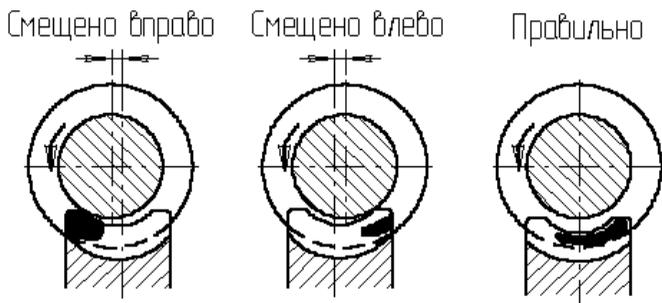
Виды отпечатков на зубьях червячного колеса при проверке зацепления на краску
